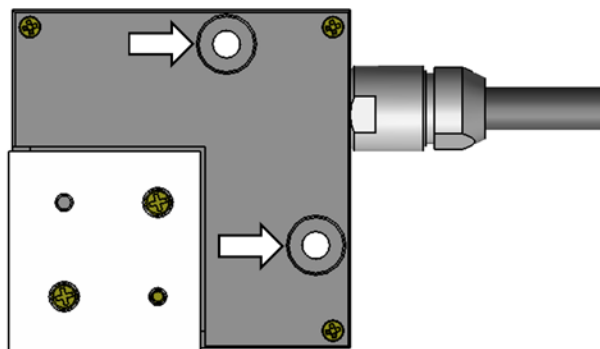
Senkbohrungen \varnothing 3,2 mm / \varnothing 6,5 mm zum Befestigen des P-616
